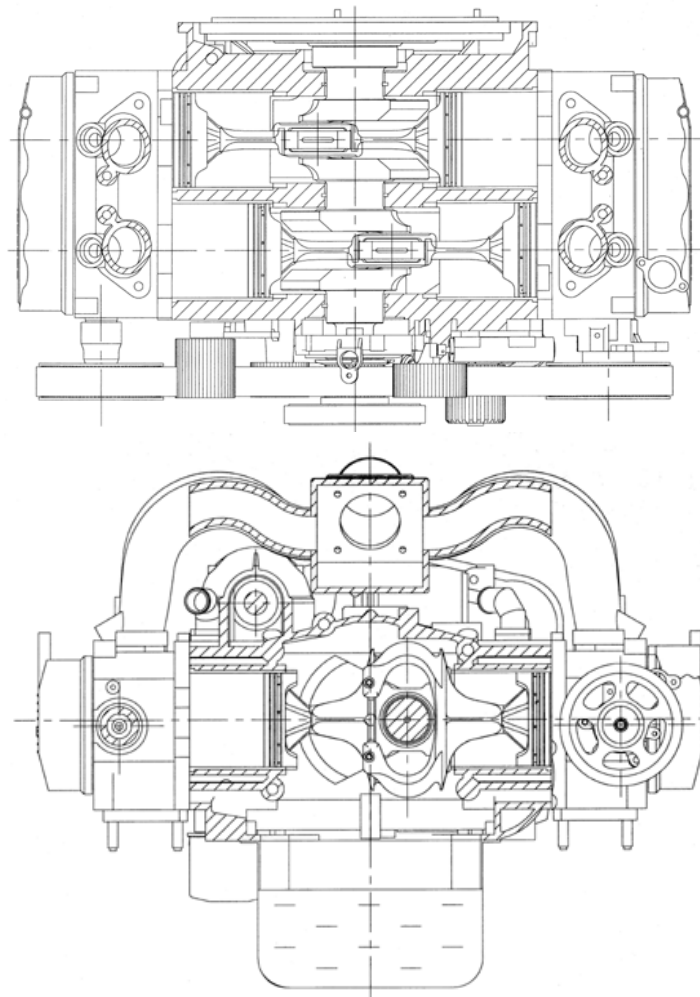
Der 2,2-l-Vierzylinder Scotch-Yoke-Motor CMC 422
